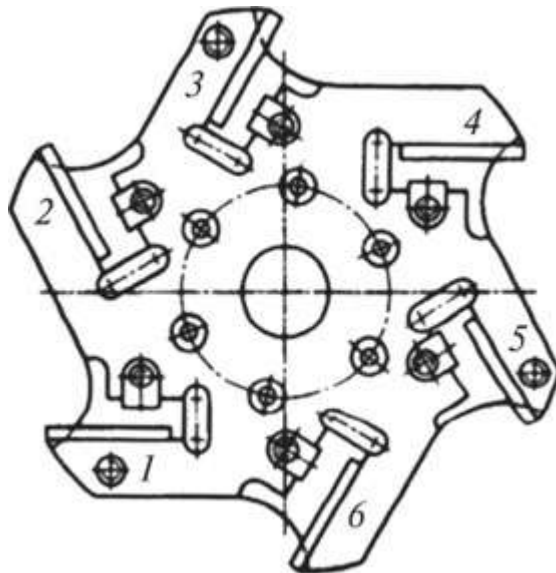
Схема 6-ти позиційної револьверної головки
